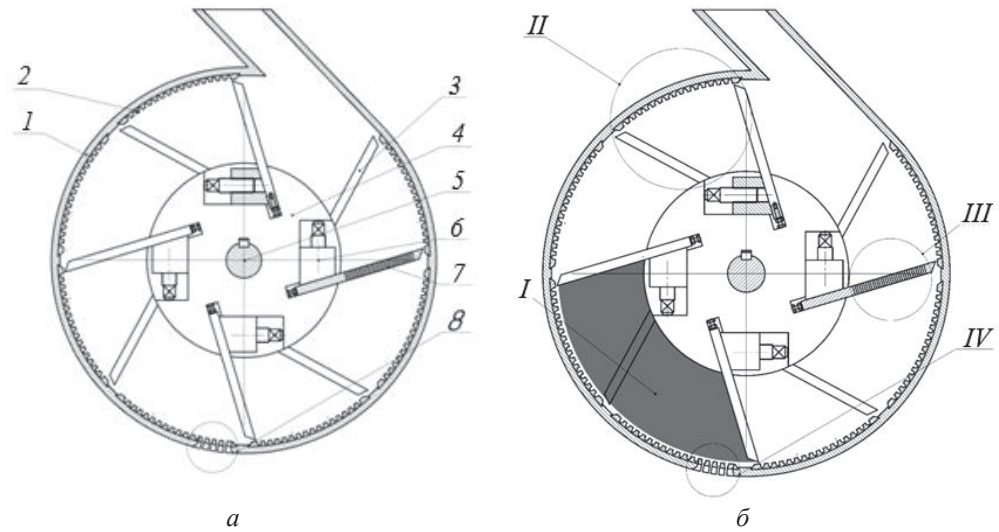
Размольная камера планко-крестовой мельницы (а) с указанием зон размола (б): 1 – корпус размольной камеры; 2 – рифленая планка статора; 3 – нож ротора; 4 – корпус составной гарнитуры ротора; 5 – вал ротора; 6 – прижимная планка; 7 – ножевые отверстия сепараторов ножей ротора; 8 – ножевые отверстия сепараторов рифленой планки; I–IV – зоны
